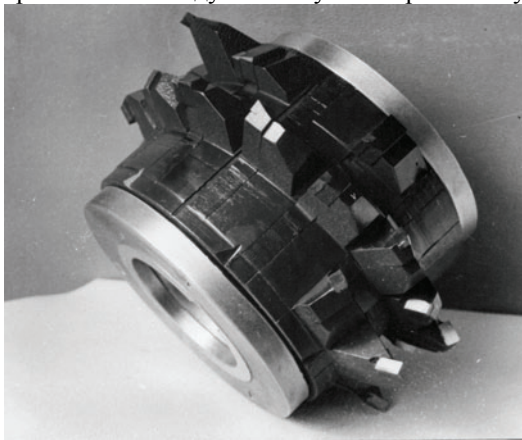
Схема фрезы с настроечным перемещением зубчатых реек.
